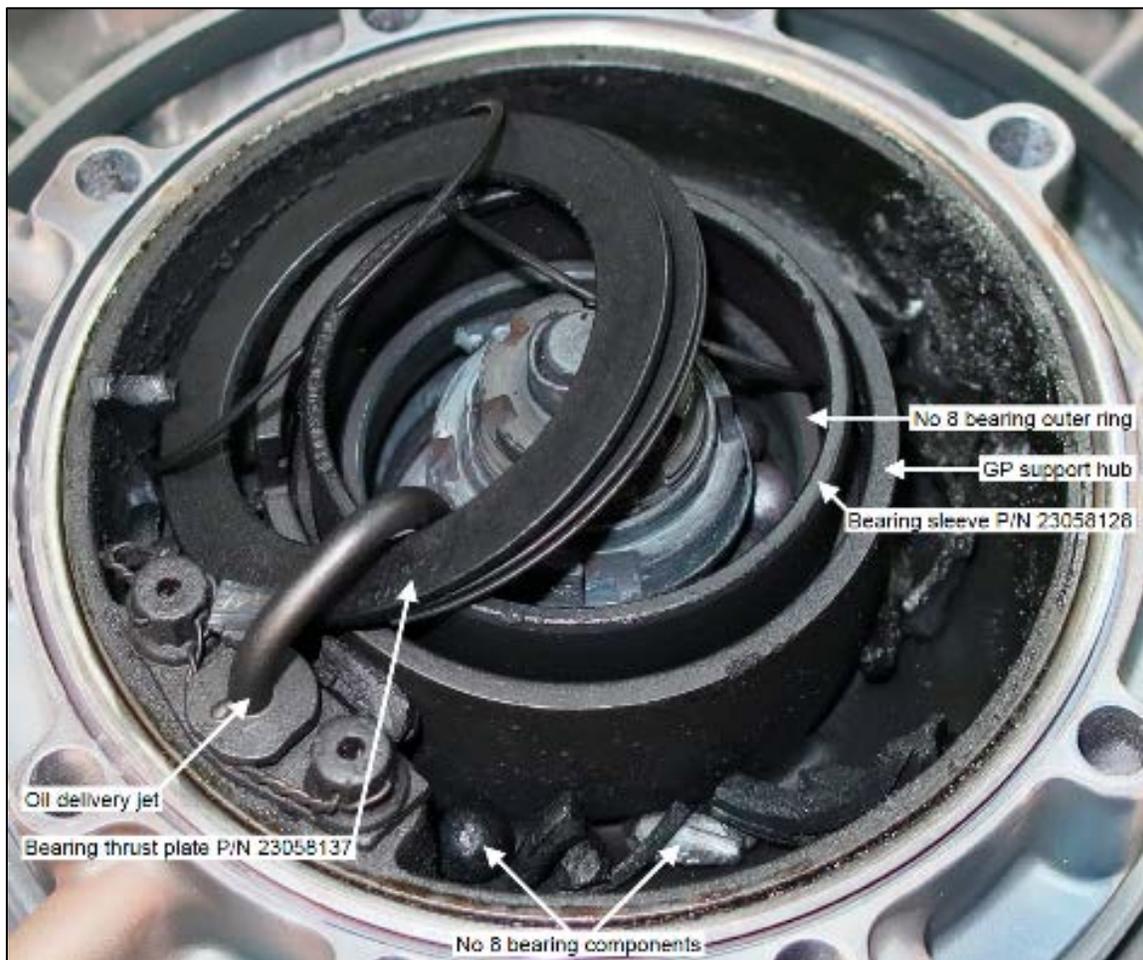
Condición del cojinete No. 8 y sus componentes.
